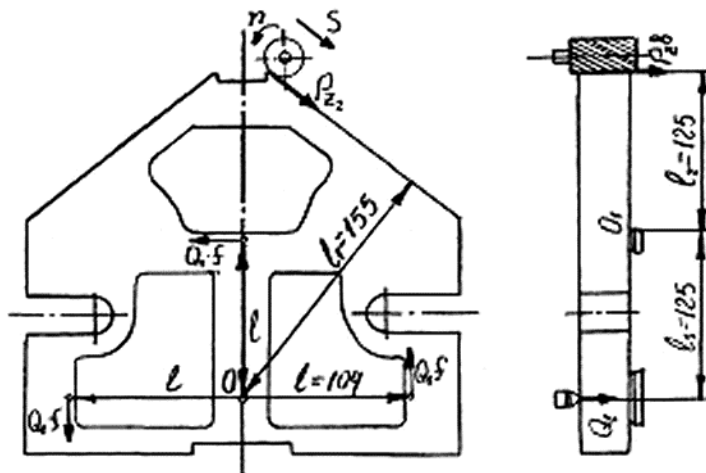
Розрахункова схема фрезерно-свердлильного пристрою
